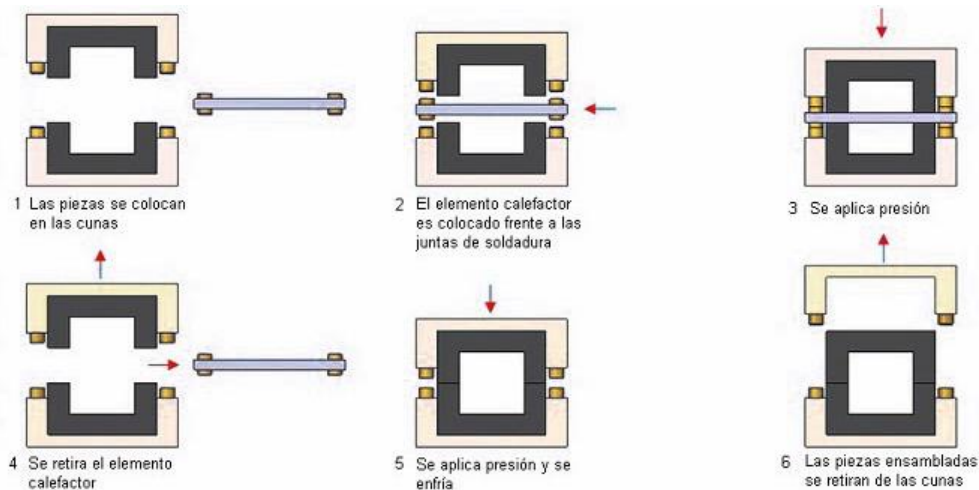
Método de soldadura por placa caliente [10].
